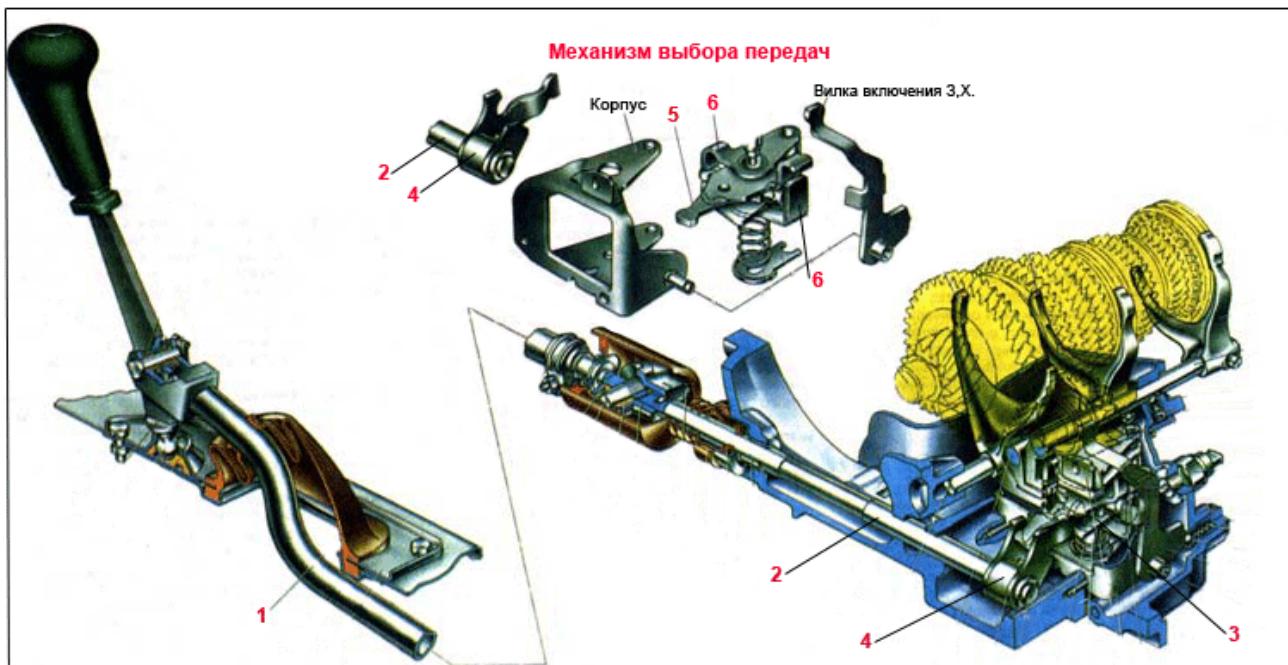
Механизм переключения передач двухвальевой коробки передач автомобиля ВАЗ
